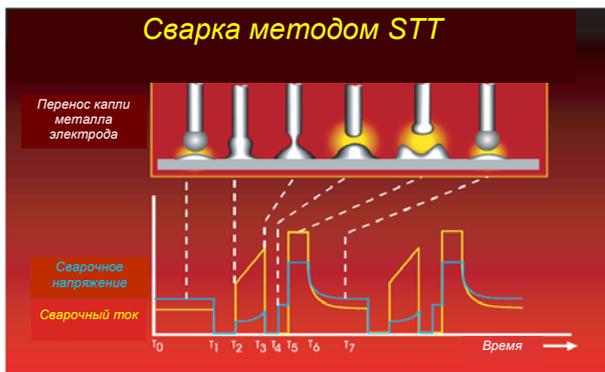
Формы кривых сварочного тока и напряжения при полуавтоматической сварке методом STT.
